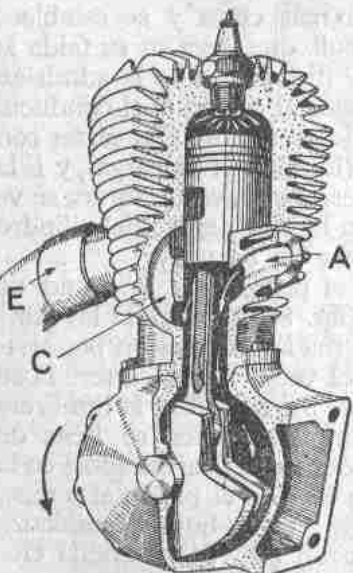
Explosión en el cilindro. Sigue la admisión en el cárter.
